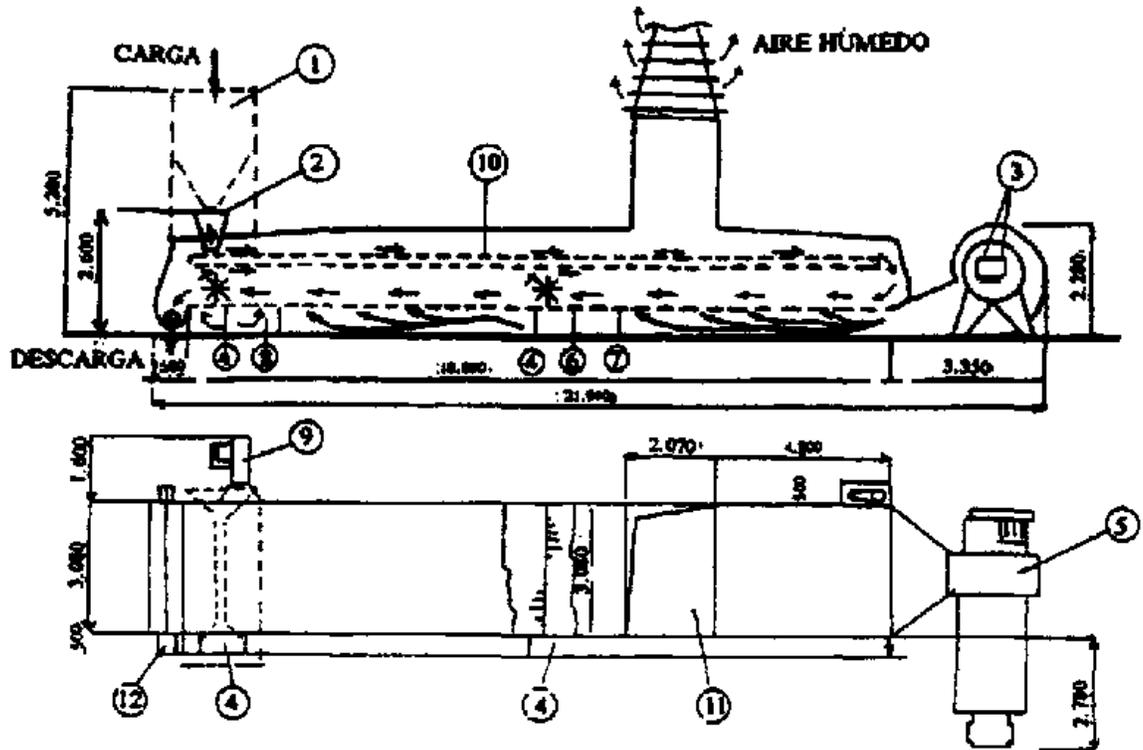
Secadora horizontal de lecho fijo, plano doble
